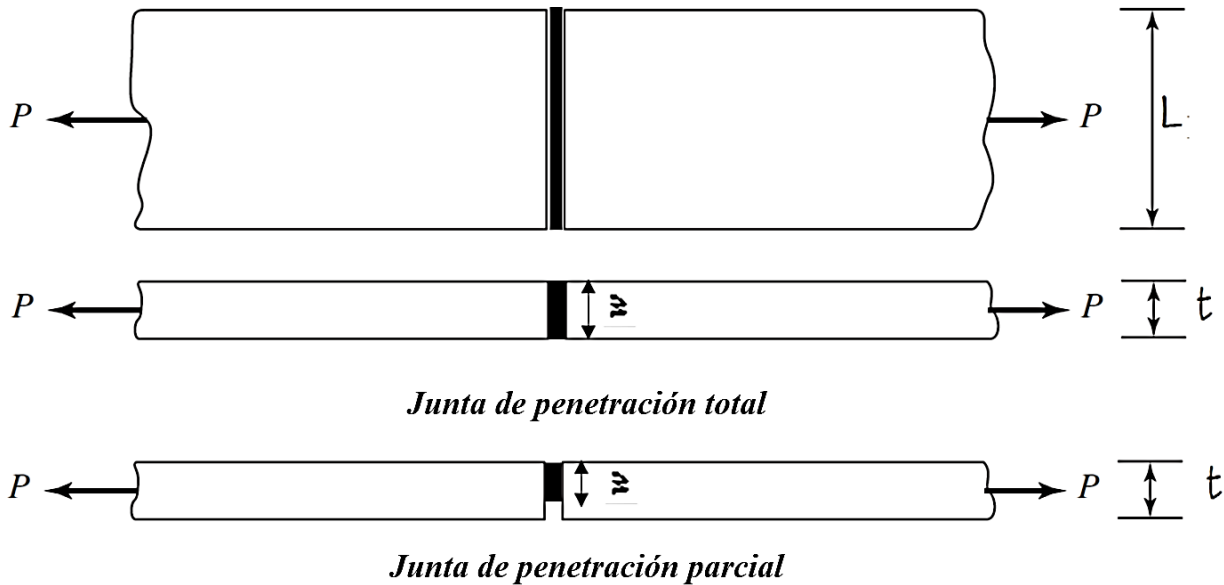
Junta de penetración total (CJP) y junta de penetración parcial (PJP) en soldaduras de ranura
